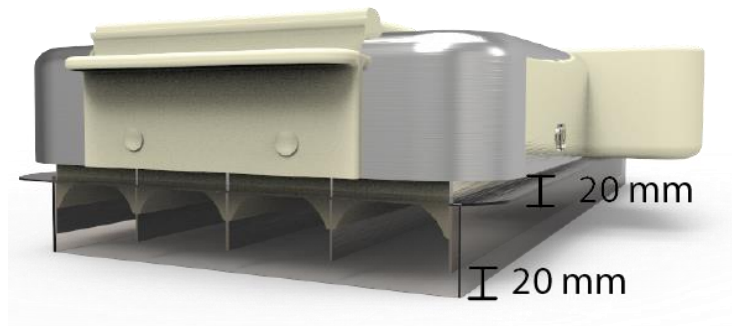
Mecanismo de compresión de masa justificativo de la altura del bastidor
